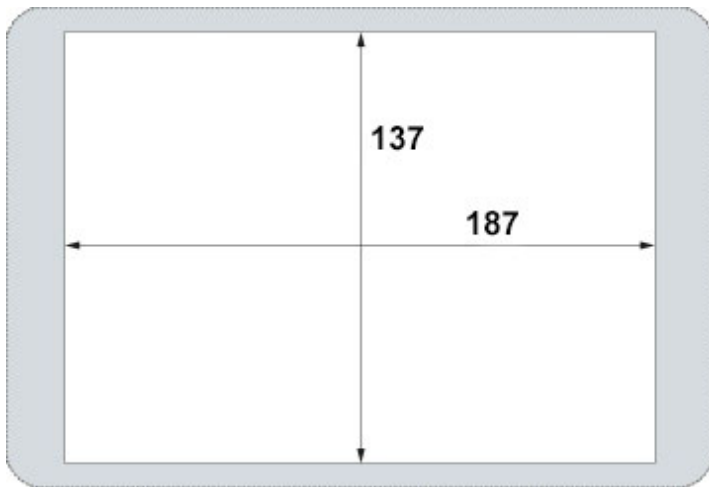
Découpe de montage GUI607 (dimensions en mm)
